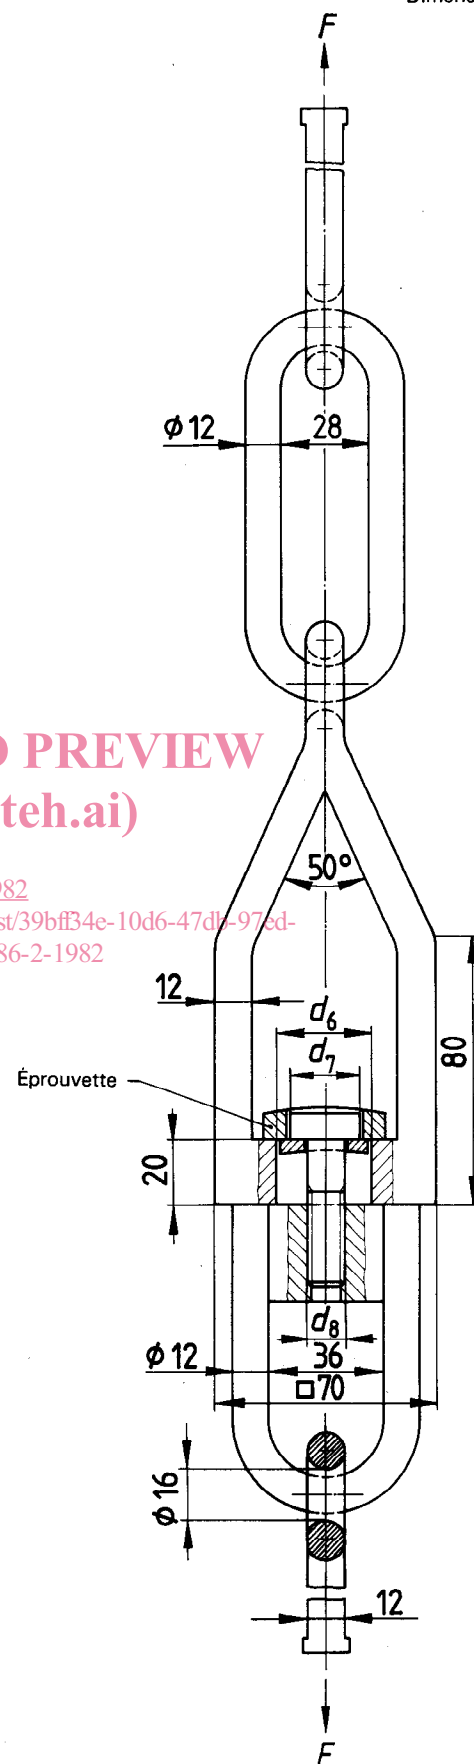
Exemple de dispositif pour l'essai de traction (T)
